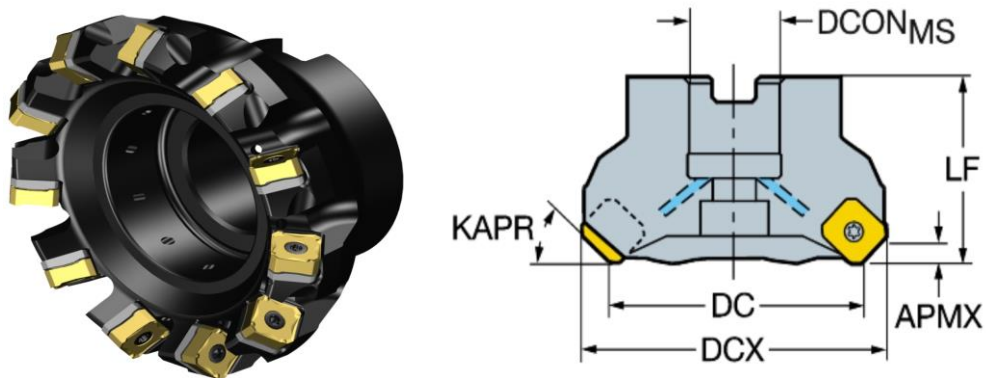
Фреза торцева Sandvik Coromill 345 з гвинтовим кріпленням пластинок[14]
